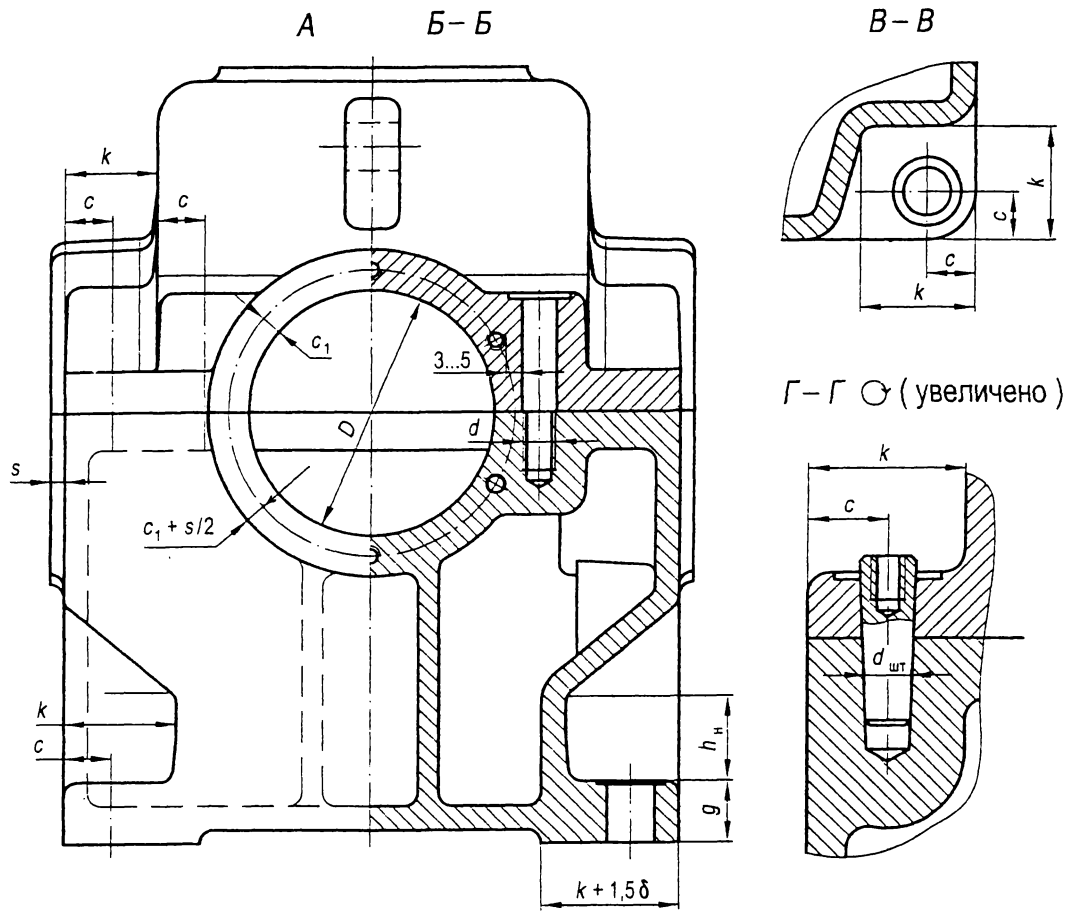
Варианты установки винтов крепления крышки к корпусу:
